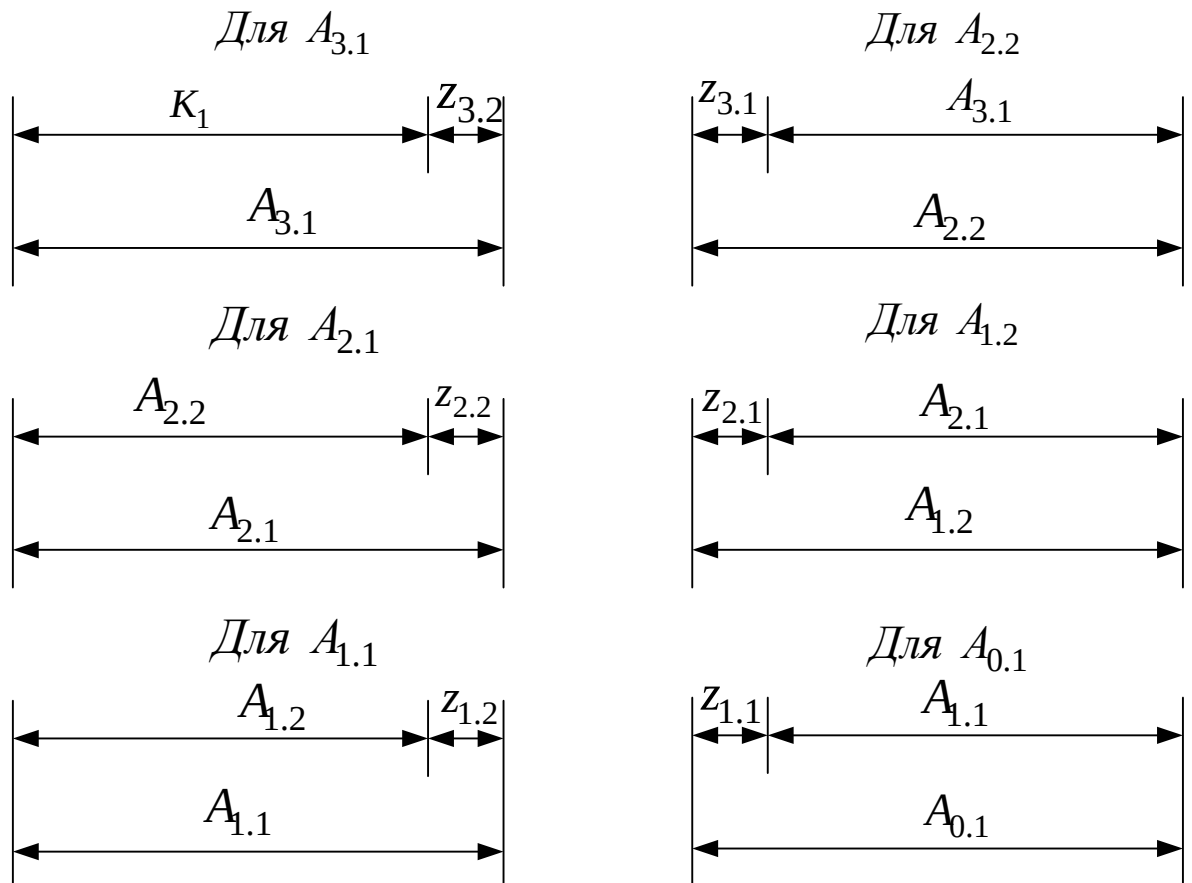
Размерные схемы ТП механической обработки зубчатого колеса
